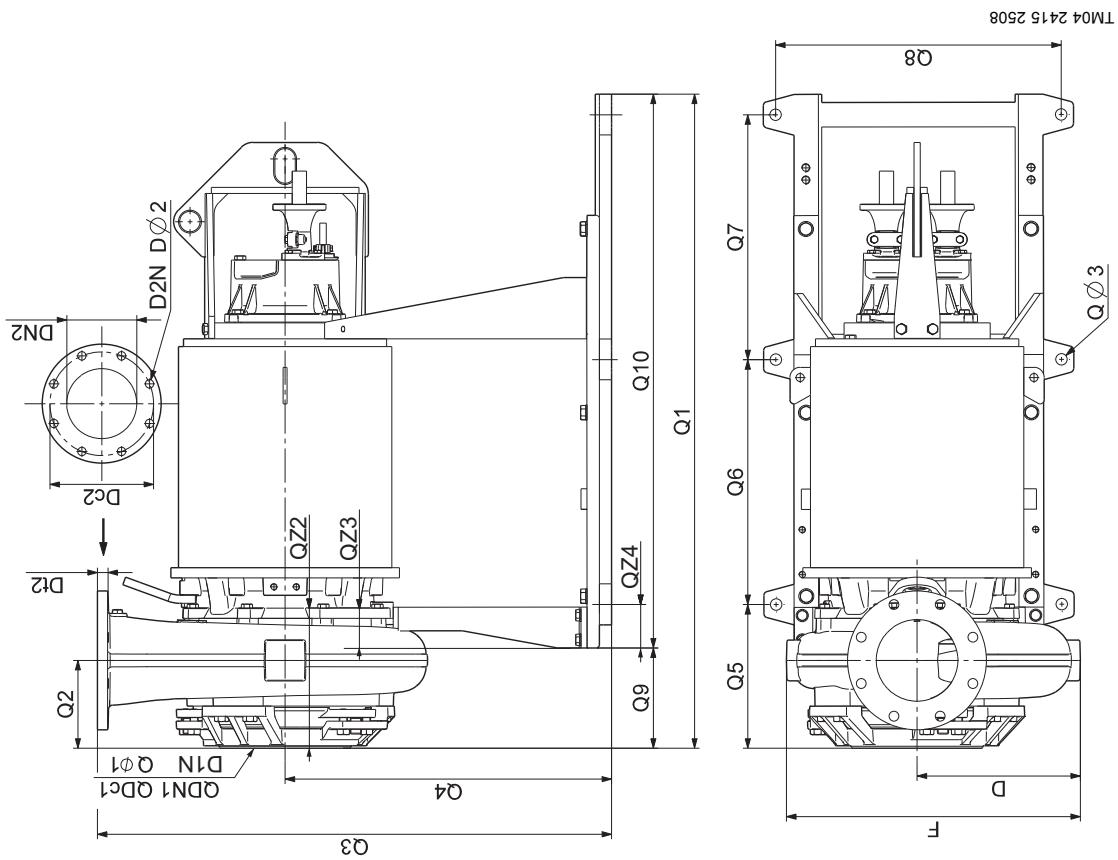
Габаритные размеры, сухая горизонтальная установка на опоре
